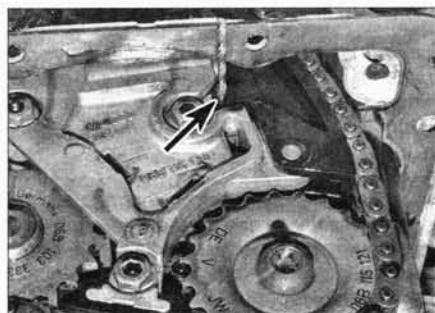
Блокировка натяжителя хвостовиком сверла
